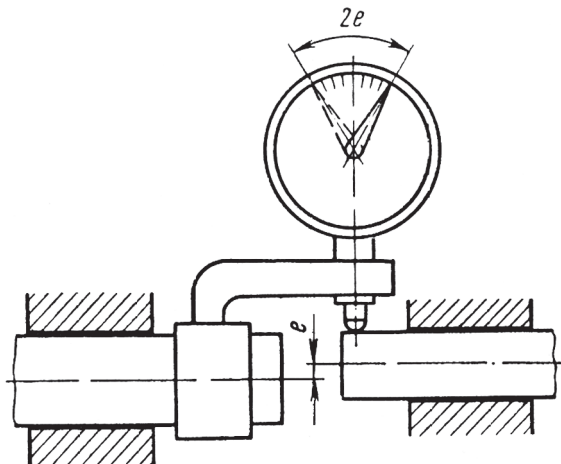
Проверка соосности валов приспособлением с индикатором
